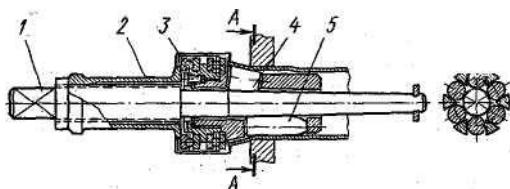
Вальцовки бортовочные ВБ. Общий вид
